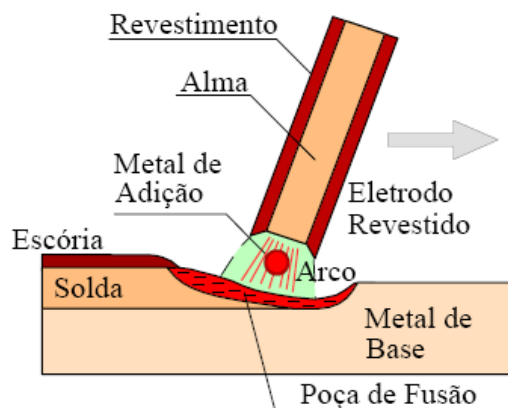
Esquema básico do processo de soldagem com eletrodo revestido [10].
